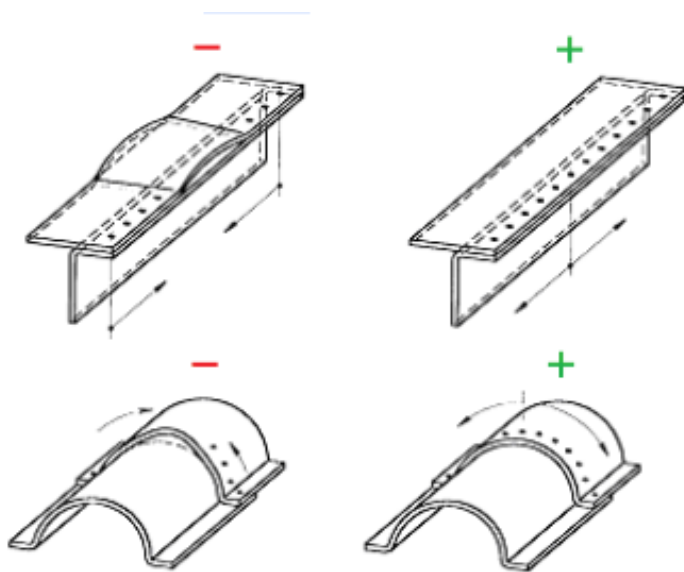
Representação do Impacte de diferentes sequências de pontos de soldadura
